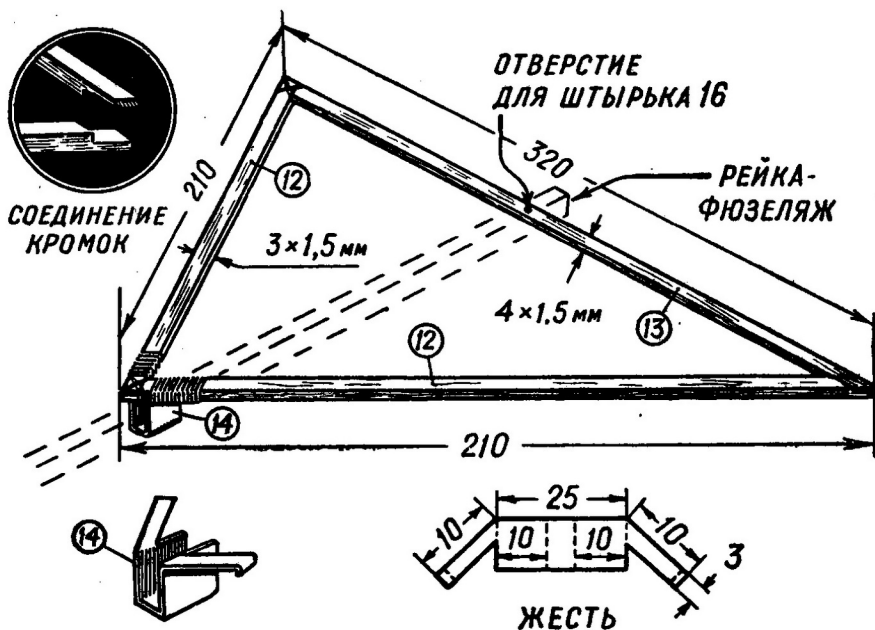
Стабилизатор модели планера и его крепление к рейке.
